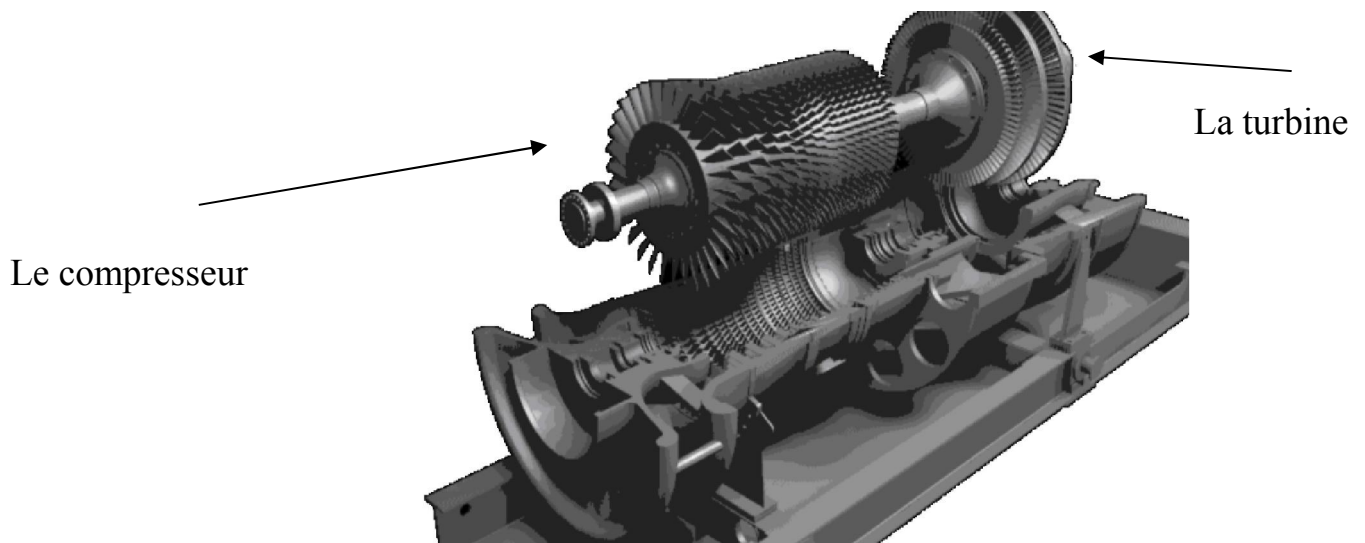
Extraction la ligne d'arbre turbo compresseur
